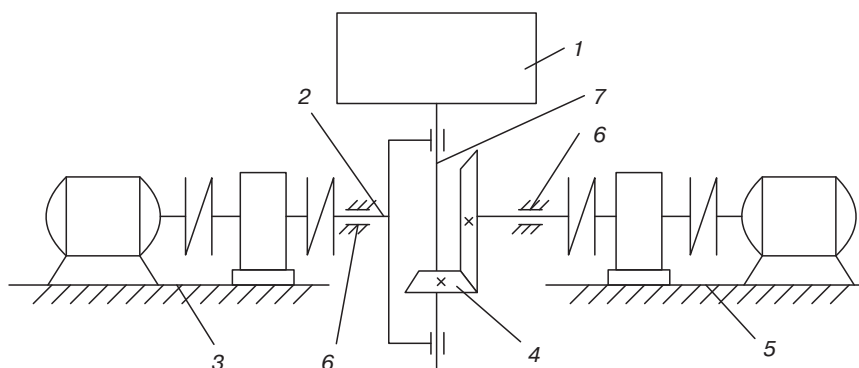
Схема машины для ротационного формования: 1 — форма; 2 — главная ось вращения; 3 — привод главной оси; 4 — коническая зубчатая передача; 5 — привод вспомогательной оси; 6 — подшипники; 7 — вспомогательная ось вращения
